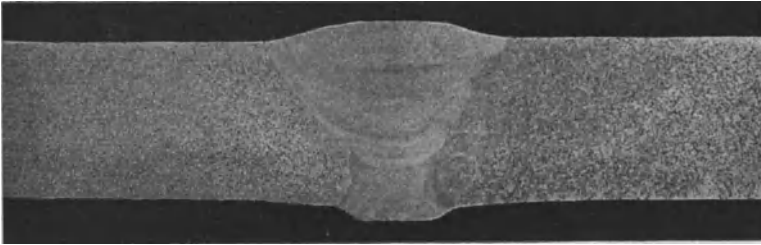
Makroaufnahme einer Höchstdruckonderschweißnaht.
